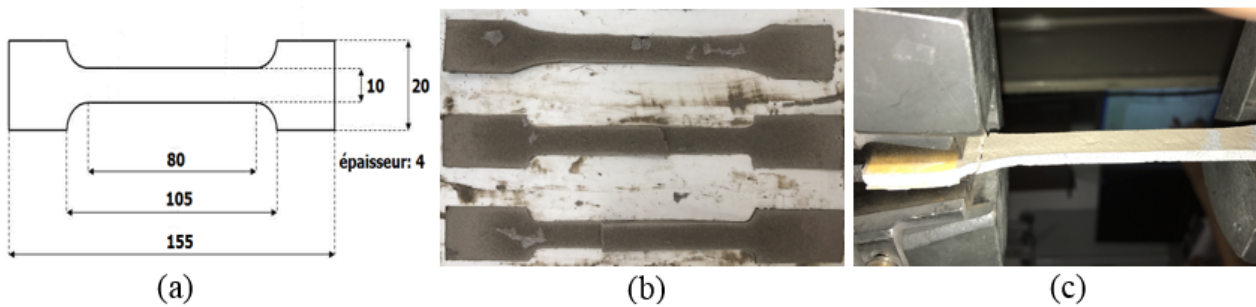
(a) Dimensions des éprouvette haltères en mm ; rupture des éprouvettes pendant le démoulage (b) et leur mise en place dans la machine de traction (c)
